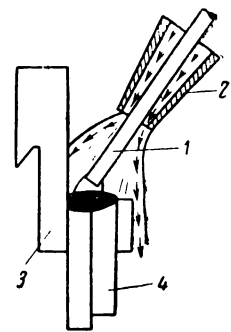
Сварка обмотки с коллектором.
